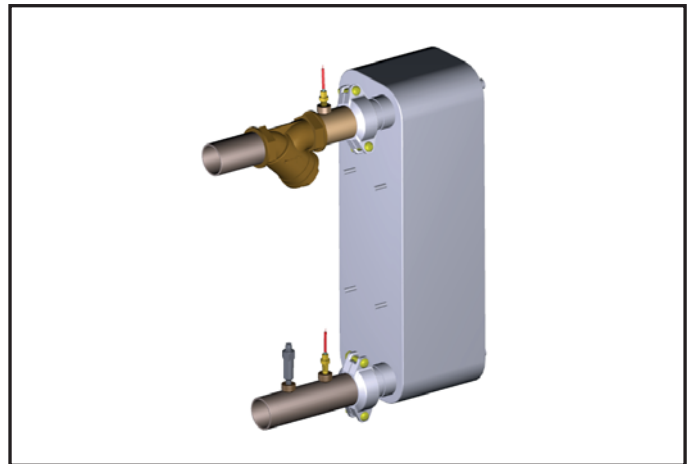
Kit de Conexão Solda-Victaulic com Filtro Y;
